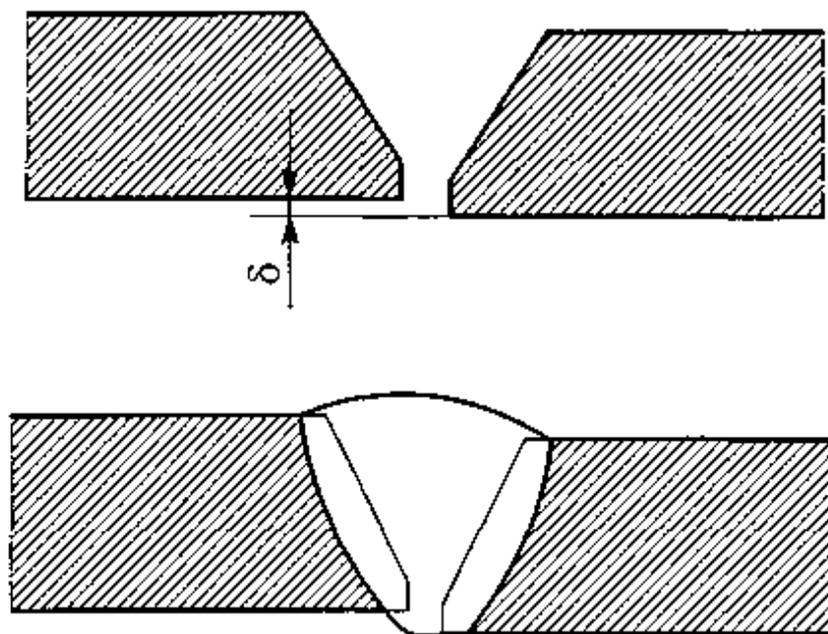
Смещение кромок в сварном соединении
